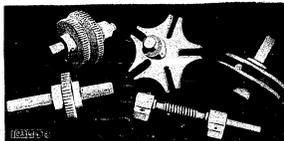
Einzelteile für Getriebe (Zahnräder, Malthesekreuz, Spindel)
